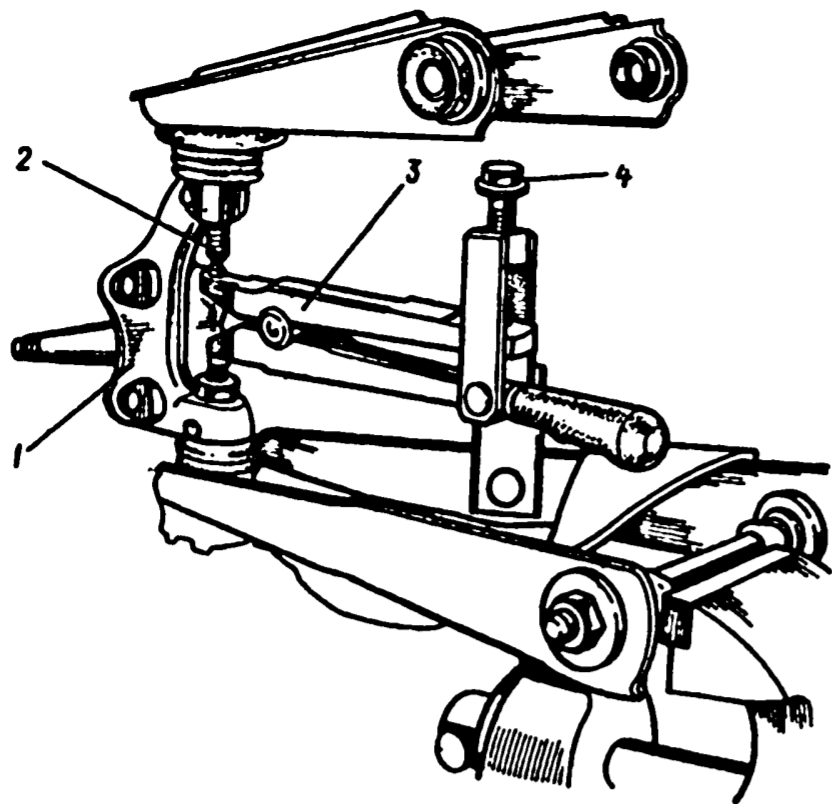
Отсоединение верхнего рычага: 1 - поворотный кулак; 2 - палец шарового шарнира; 3 - приспособление 67.7801.9513; 4 - болт
